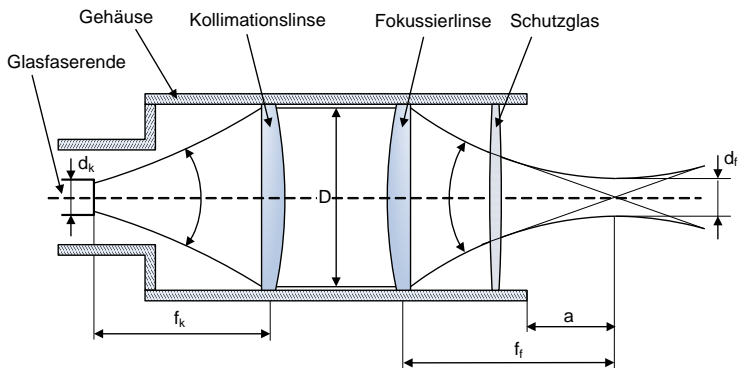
Prinzipieller Aufbau einer transmissiven Bearbeitungsoptik zum Laserstrahlschweißen mit Festkörperlasern
